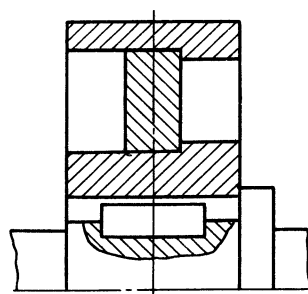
Сварная сборочная единица на сборочном чертеже
